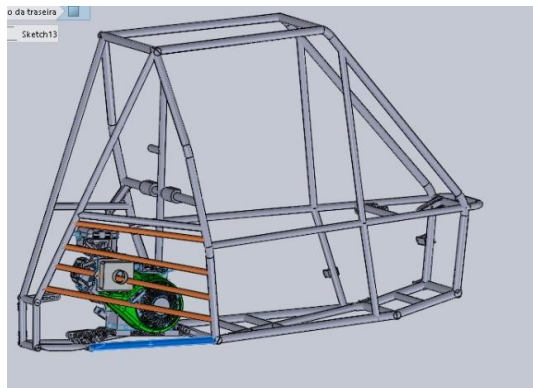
Tubo inferior (azul) e plano parcial do envelope (laranja)
